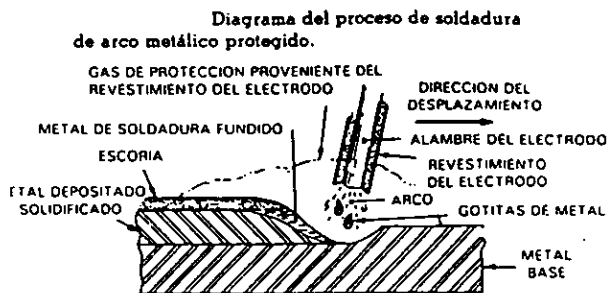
Proceso de soldadura de arco metálico protegido.
